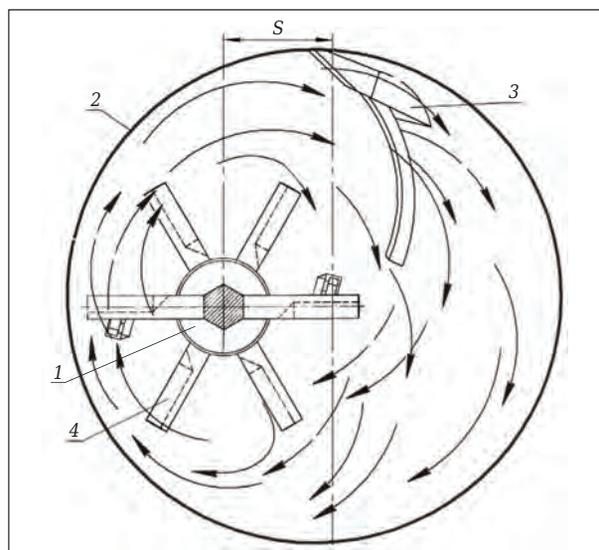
Основные конструктивные параметры смесителя: 3 — донно-боковой скребок; 4 — лопатки; остальные обозначения — в тексте
